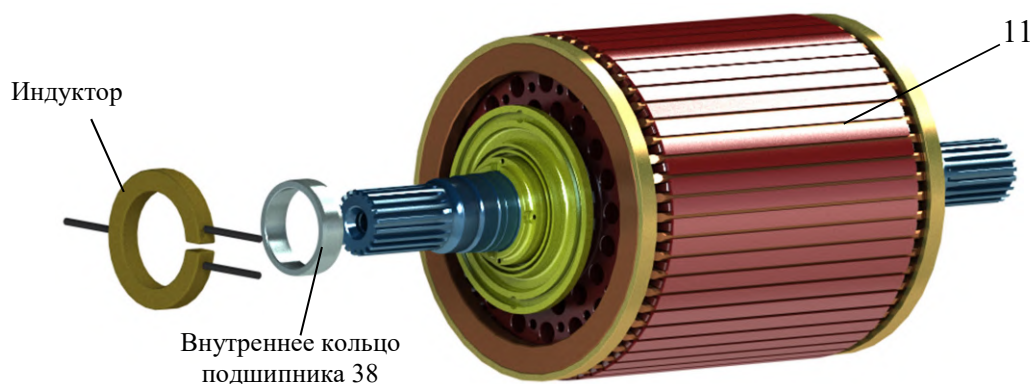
Монтаж внутреннего кольца подшипника со стороны привода на вал ротора
